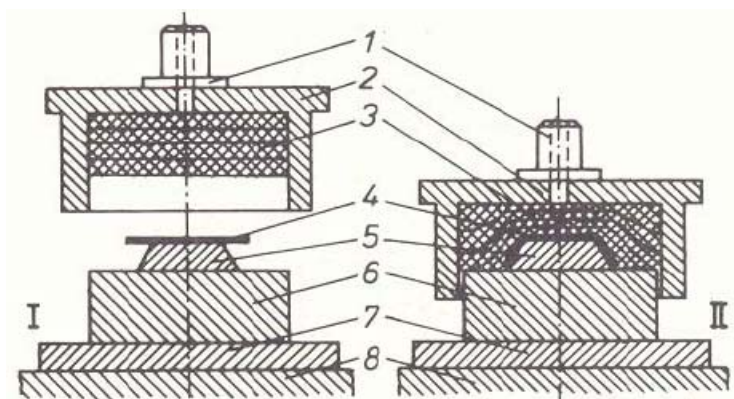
Nástroj pro ztenčování a rozšiřování pružným tažníkem [3]
